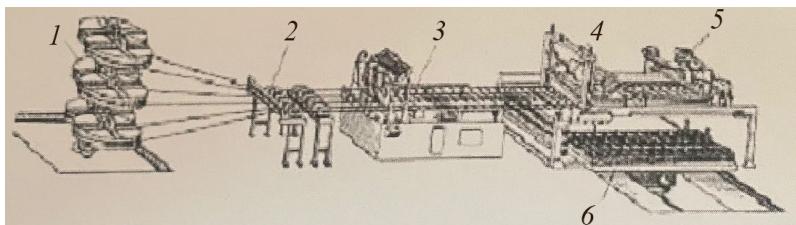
Общий вид автоматизированной линии 7728А/3 для изготовления арматурных сеток шириной до 775 мм: 1 – бухтодержатель СМЖ-323А; 2 – правильное устройство СМЖ-324А; 3 – сварочная машина МТМК 3Х100-4; 4 – ножницы СМЖ-325А; 5 – пакетировщик 326А; 6 – тележка-контейнер СМЖ-327А
